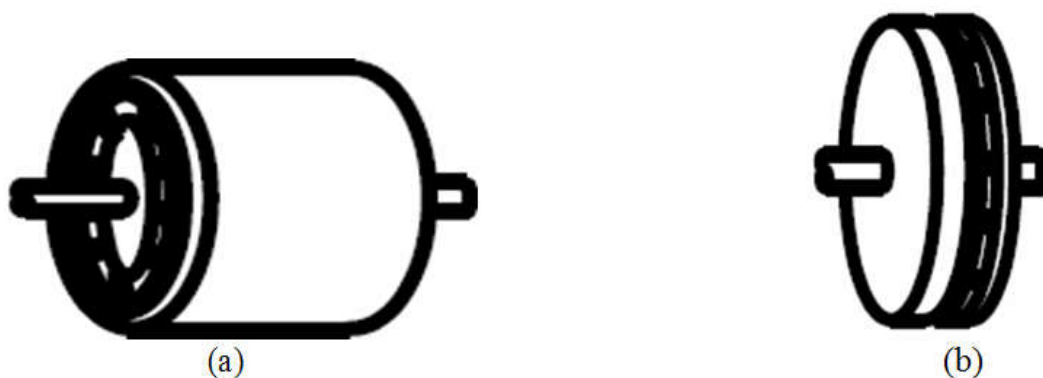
Vue schématique des machines : (a) à flux radial, (b) à flux axial [2].
